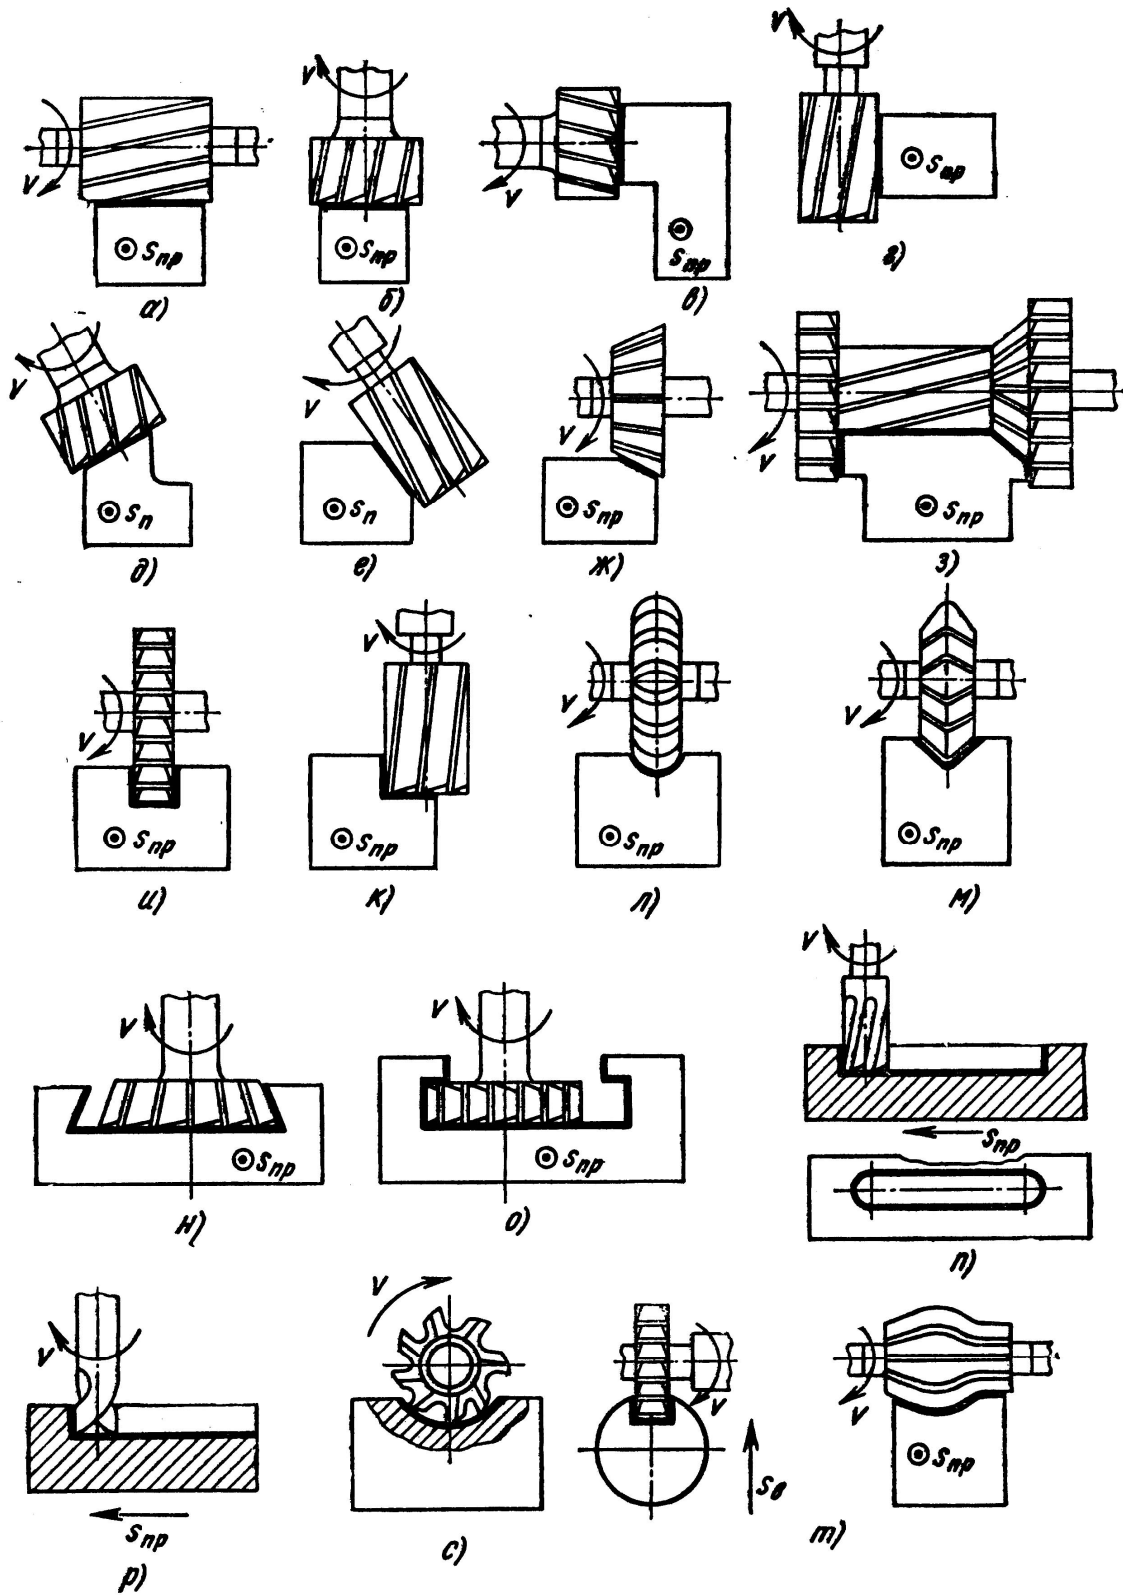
Схеми обробки поверхонь заготовок на горизонтально- та вертикально-фрезерних верстатах
